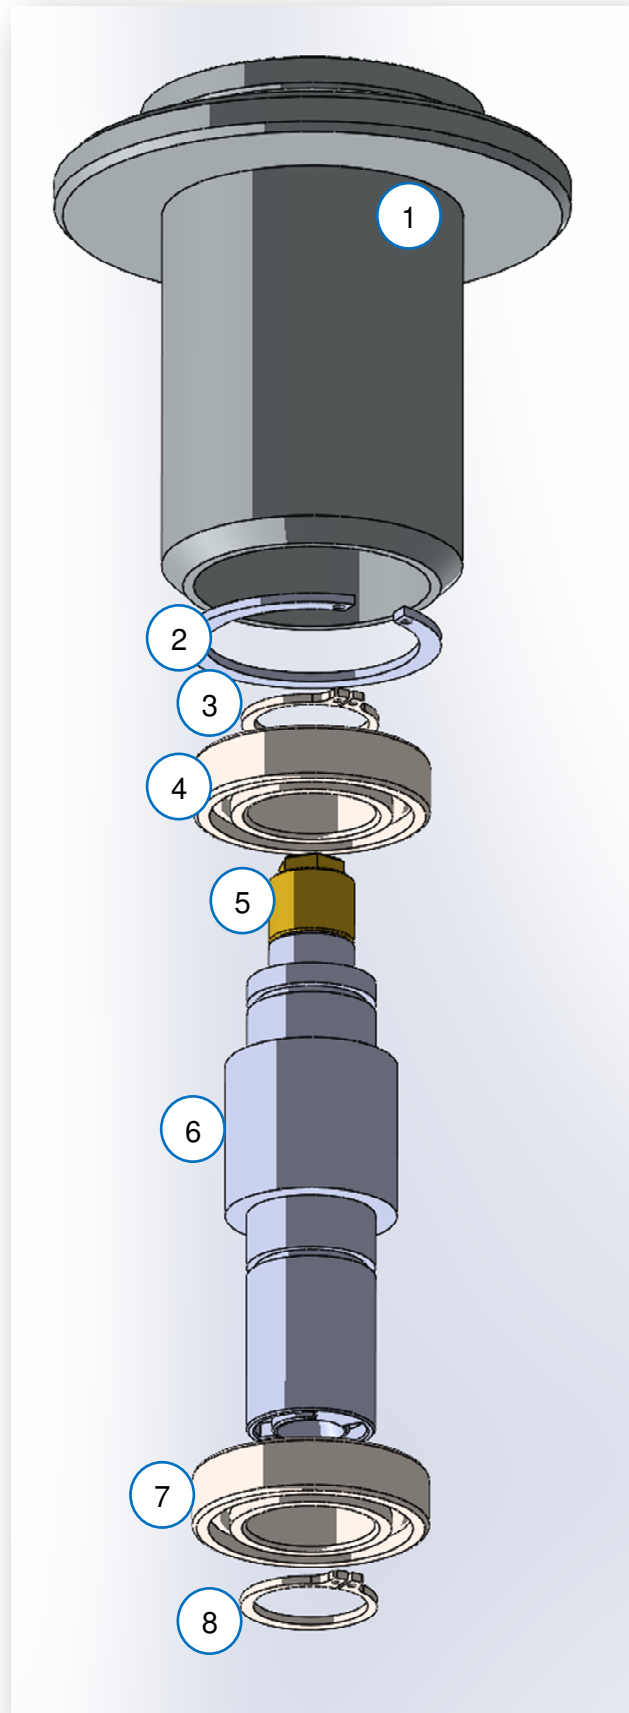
Werkzeughalter 1 Explosionsdarstellung
